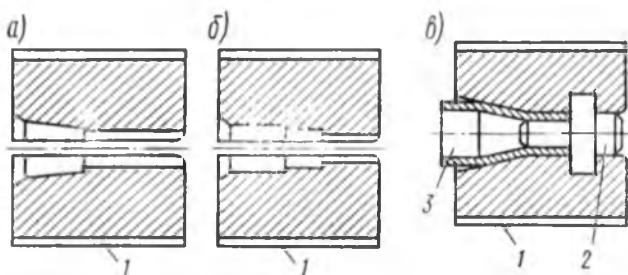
Штамповый инструмент радиально-ковочной машины дляковки одноступенчатых (а) и многоступенчатых (б) валов и трубных заготовок на оправке (в):
